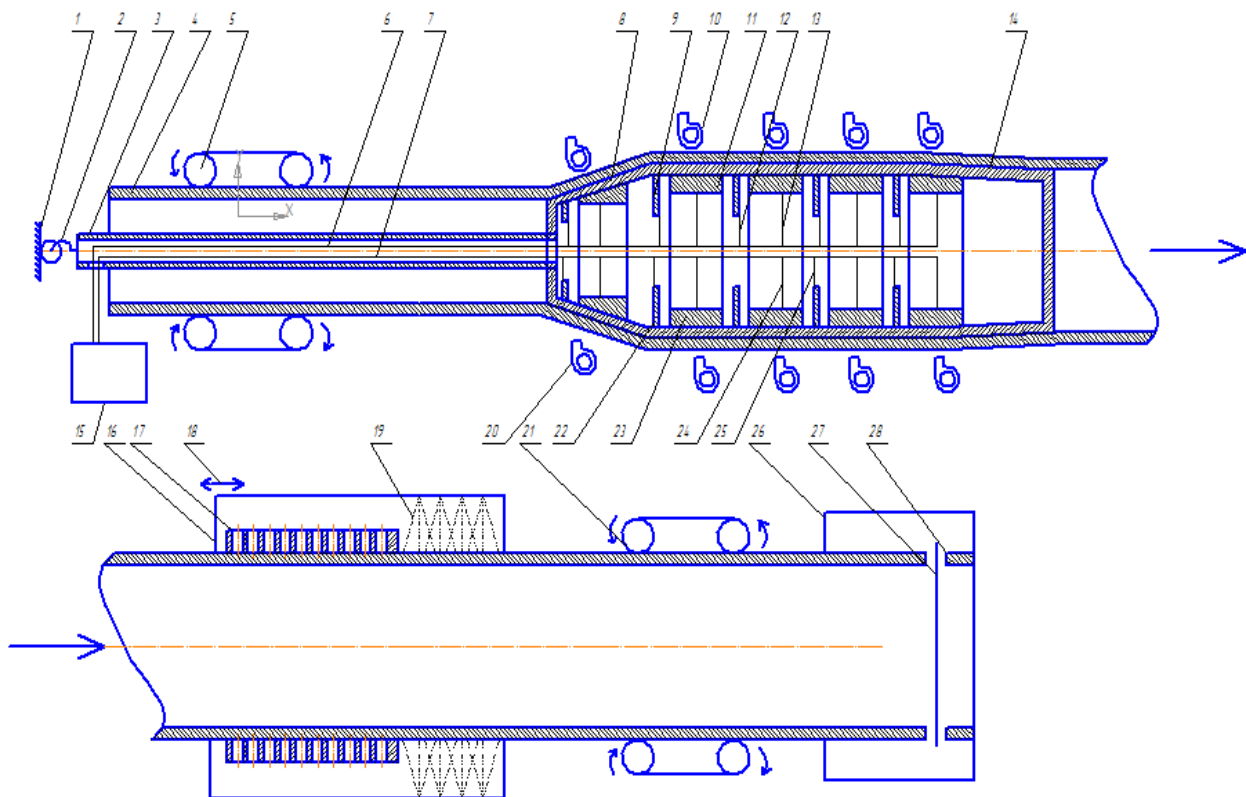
Установка №2 для виготовлення труб ПВХ-О: 1– нерухома опора; 2 – з'єднувачій елемент; 3 – трубка-тримач; 4 – труба з полівінілхлориду; 5 – штовхаючий пристрій; 6 і 7 – кабелі; 8 – конічна оправка; 9 – датчики температури верхнього ряду; 10 – повітродувки верхнього ряду; 11 – нагрівальні елементи верхнього ряду; 12 – кабелі датчиків температури верхнього ряду; 13 – кабелі нагрівальних елементів верхнього ряду; 14 – спадаючі частини конічної оправки; 15 – блок керування; 16 – вакуумна ванна; 17 – калібр; 18 – переміщувачі вакуумної ванни; 19 – форсунки охолодження; 20 – повітродувки нижнього ряду; 21 – тягнучий пристрій; 22 – датчикі температури нижнього ряду; 23 – нагрівальні елементи нижнього ряду; 24 – кабелі нагрівальні елементів нижнього ряду; 25 – кабелі датчиків температури нижнього ряду; 26 – відрізний пристрій; 27 – відрізний елемент; 28 – труба з полівінілхлориду після операції відрізання.
